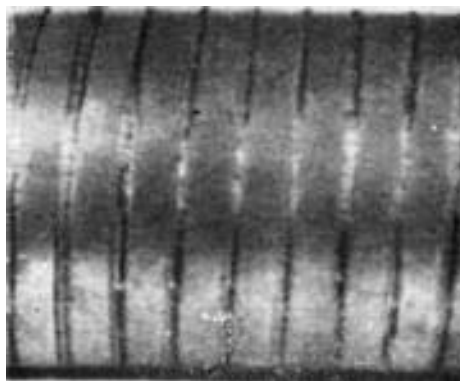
Шероховатые глубокие риски от обработки резанием, расположенные вдоль всей обработанной заготовки
